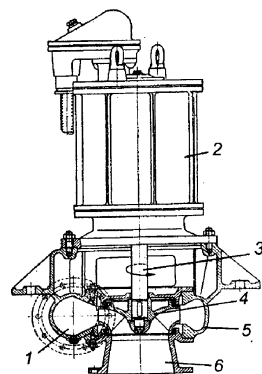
Схема водоотливного насоса: 1-напорный патрубков; 2-электродвигатель; 3-вал; 4-рабочее колесо; 5-корпус; 6-всасывающий патрубков
